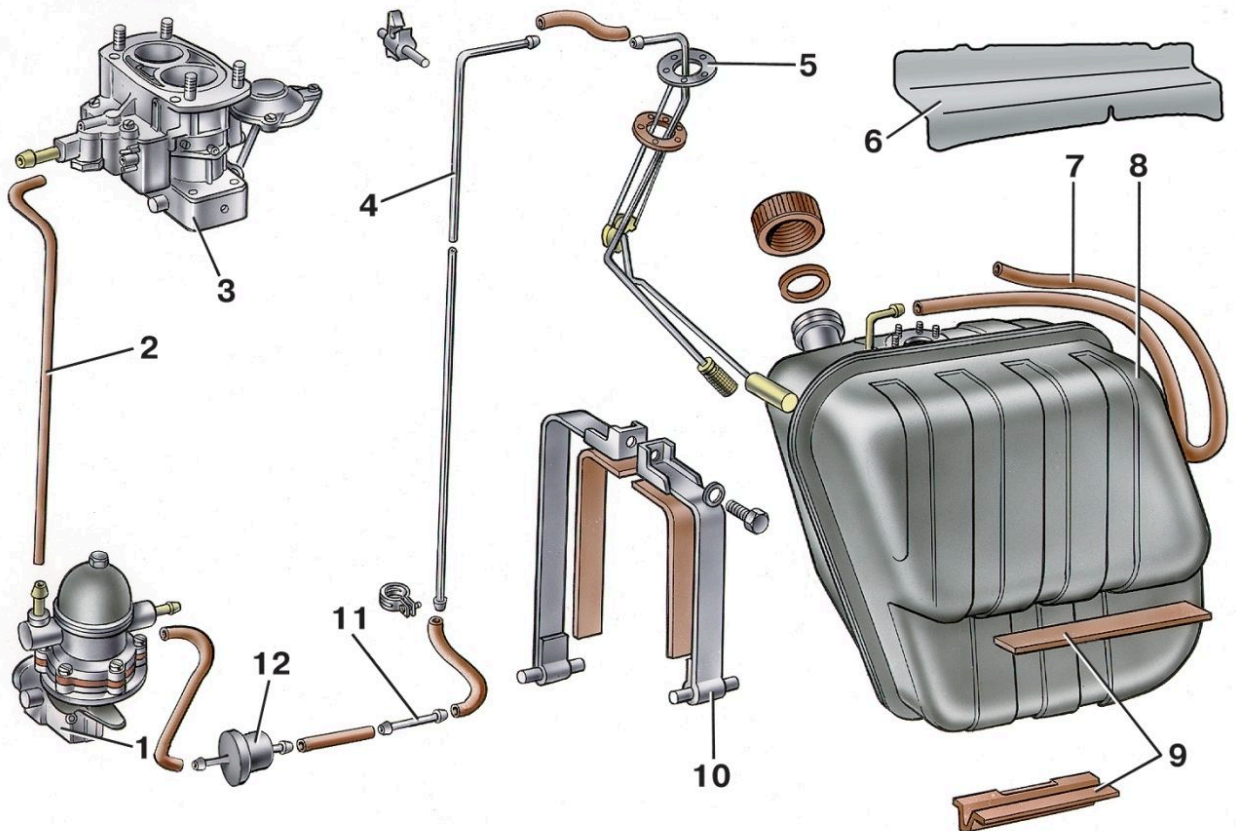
Паливний бак і паливопроводи: 1 - паливний насос; 2 - шланг від паливного насоса до карбюратора; 3 - карбюратор; 4 - задня трубка; 5 - датчик показника рівня й резерву палива; 6 - запобіжний щиток; 7 - трубка вентиляції бака; 8 - паливний бак; 9 - прокладки; 10 - хомут кріплення паливного бака; 11 - передня трубка; 12 - фільтр тонкого очищення палива
